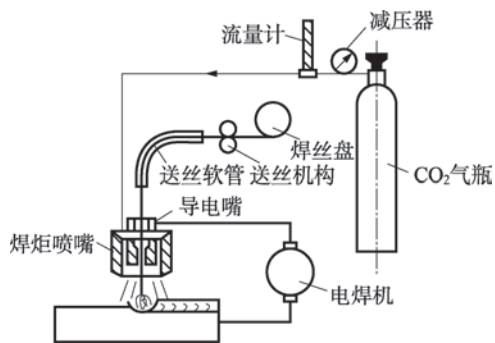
二氧化碳气体保护焊的焊接装置
